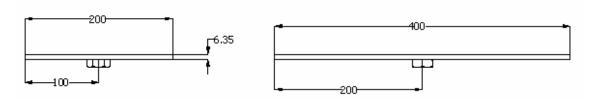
Placa de expulsión matriz 1 (Molde A)
